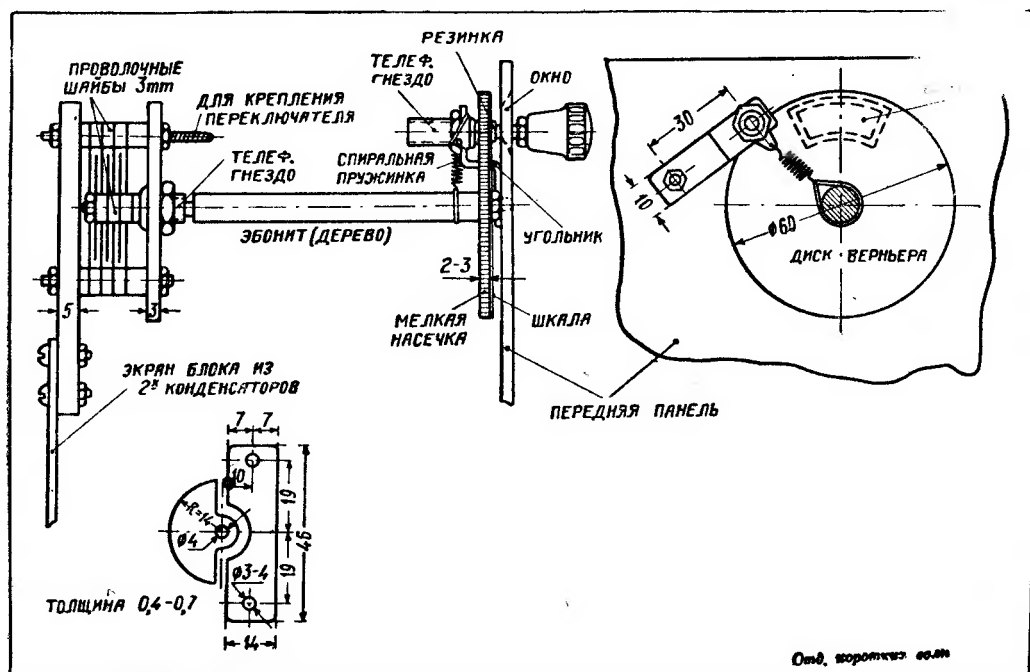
Подстроечный конденсатор с верньерным механизмом
